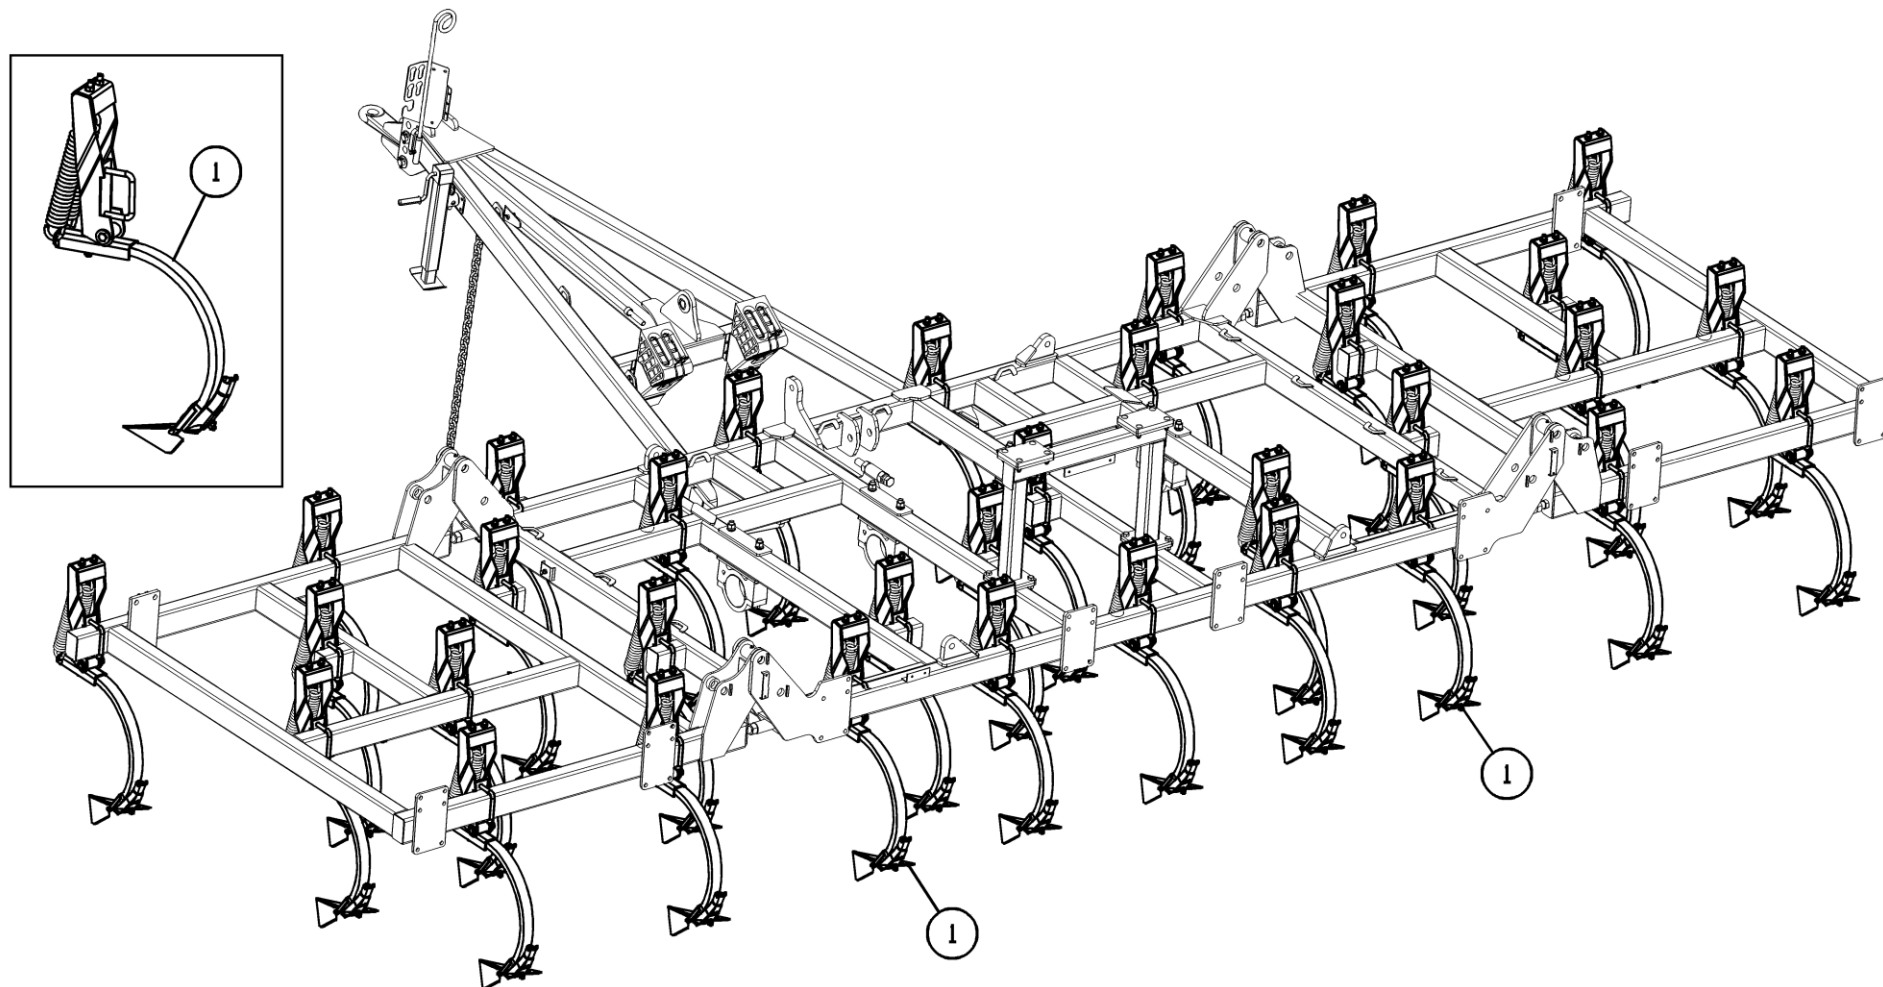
Установка рабочих органов СГ-082.03.000
